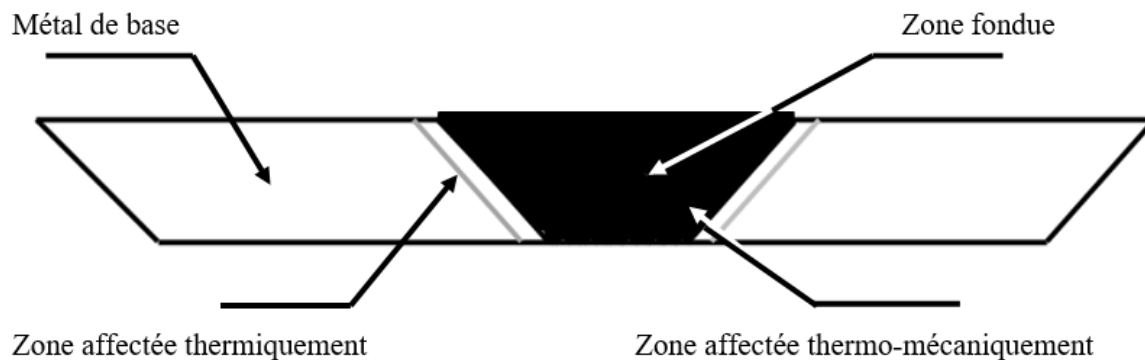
Cordon de soudure FSW d'un alliage d'aluminium 2024 T3
